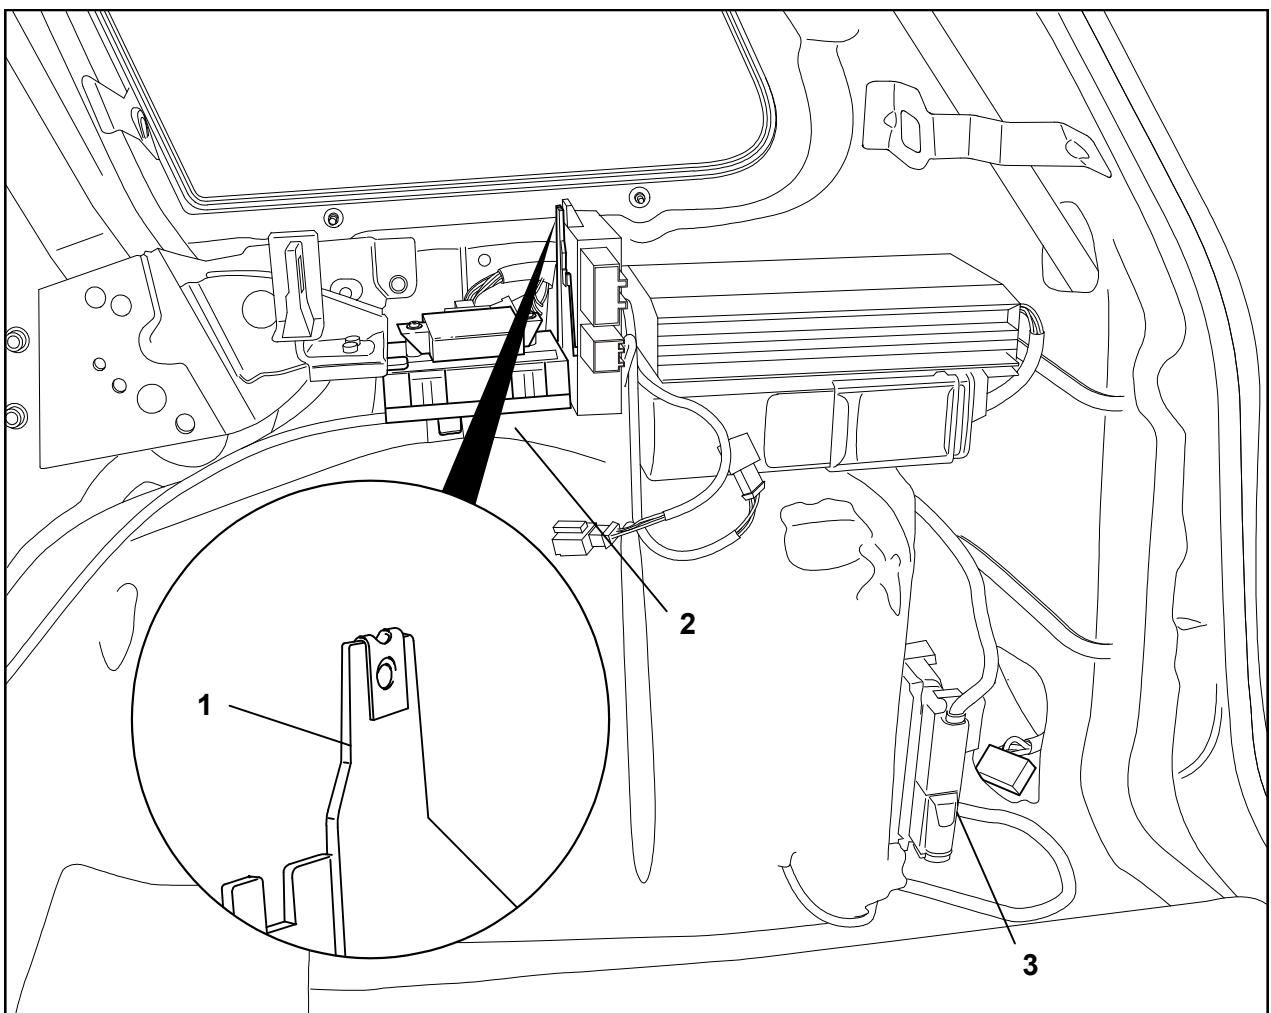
Collegare il dispositivo di collegamento rimorchio
